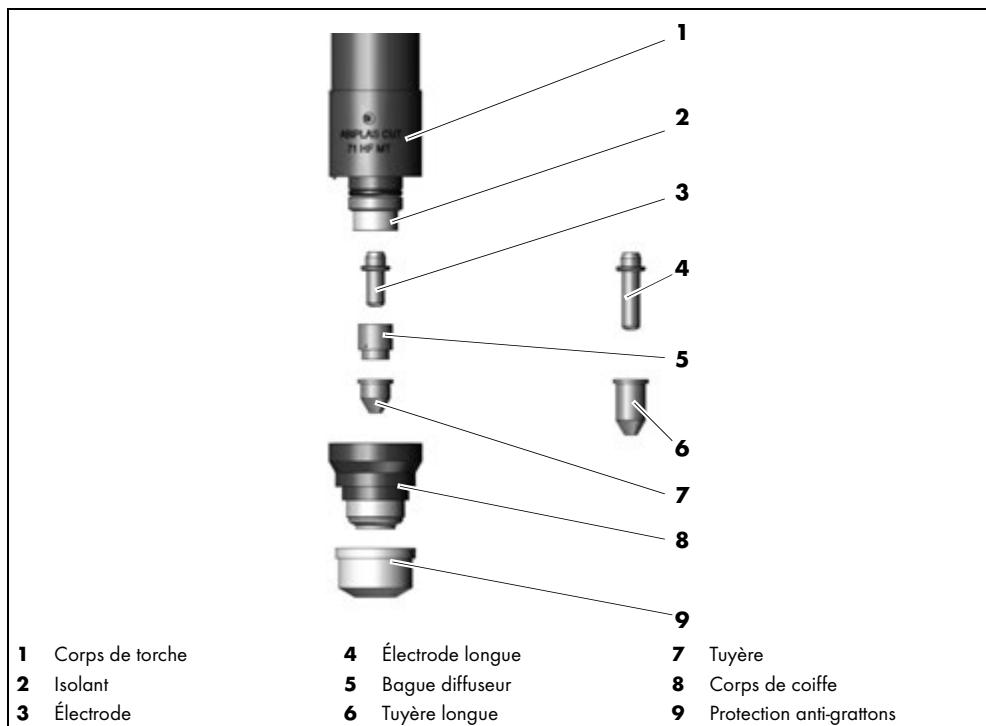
Vue d'ensemble d'ABIPLAS® CUT 151 HF
